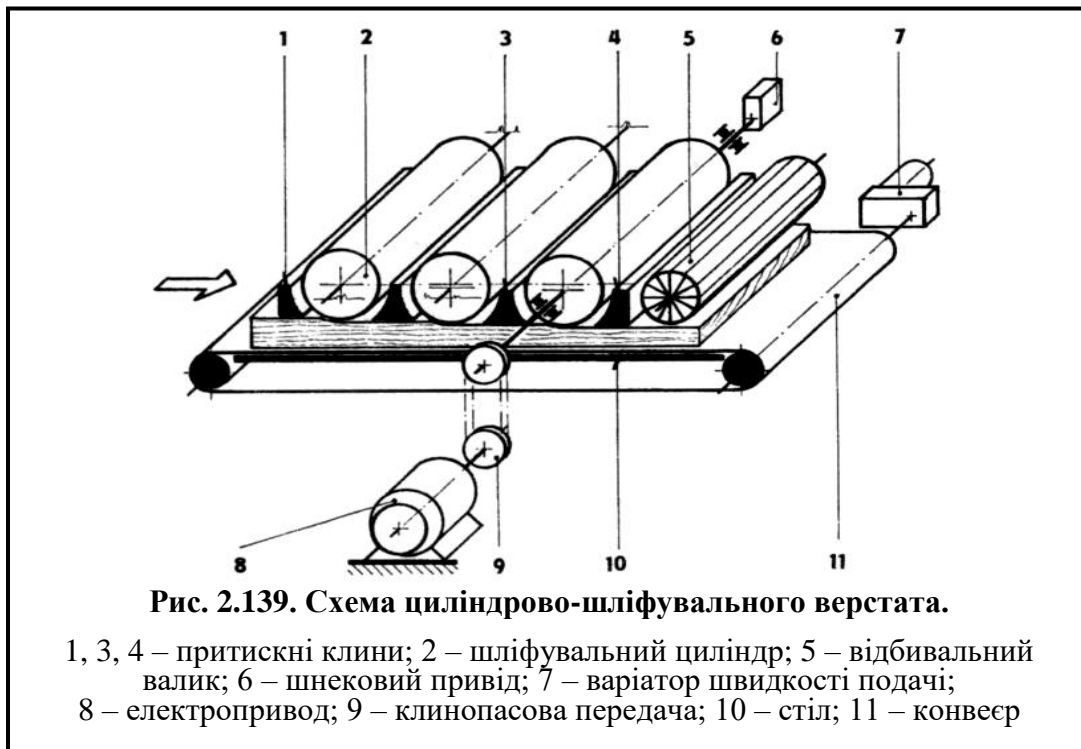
Схема циліндрово-шліфувального верстата.
